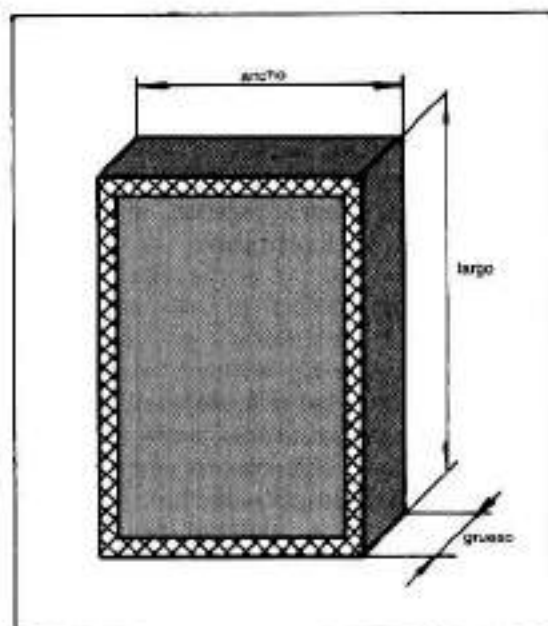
Dimensiones exteriores de un panel solar plano.
